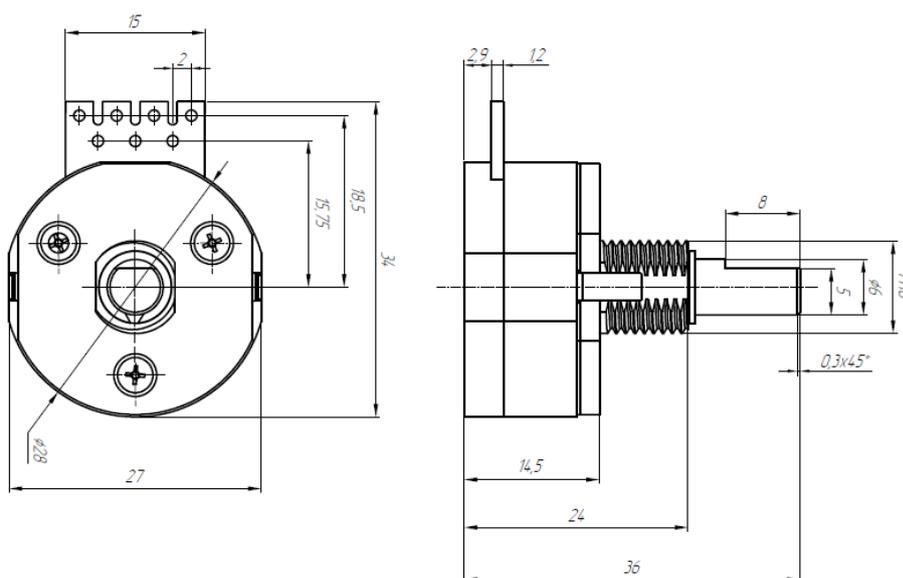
Установочные и присоединительные размеры энкодера
